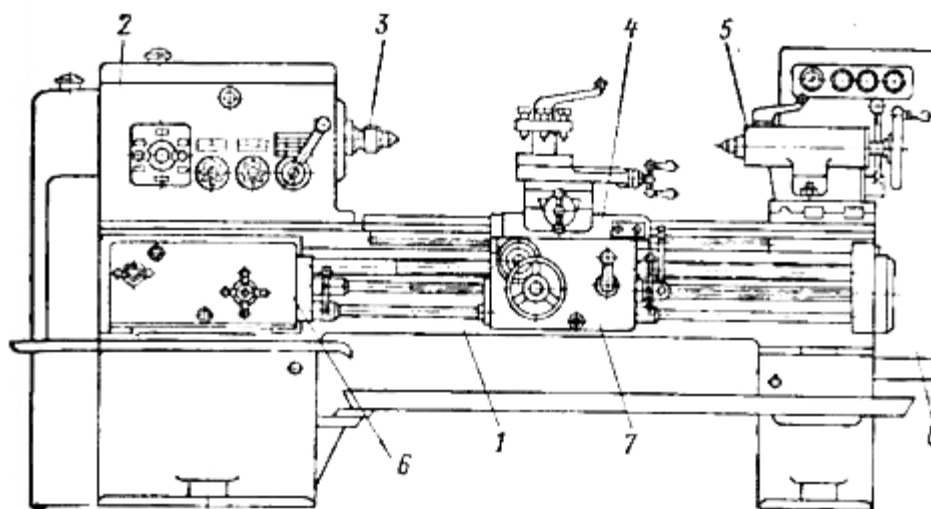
Общий вид универсального токарно-винторезного станка
